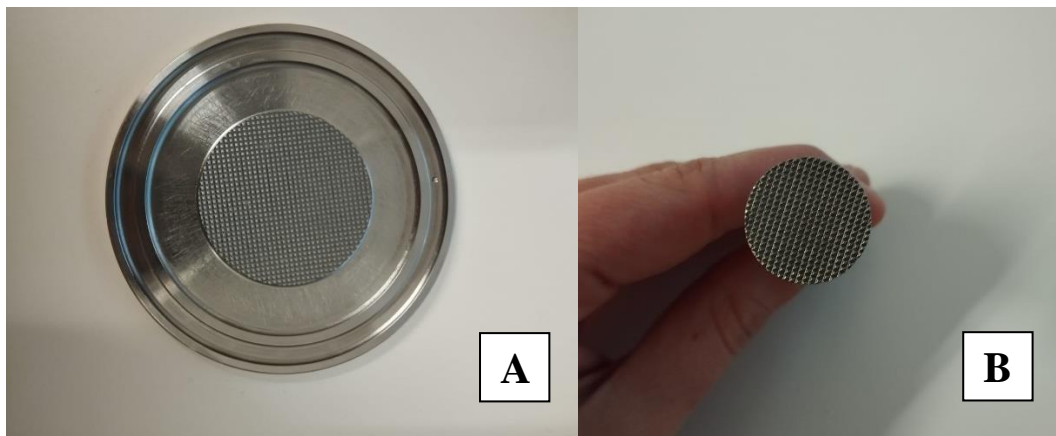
(A) Plato serrado. (B) Cono serrado. Fuente: Original.
